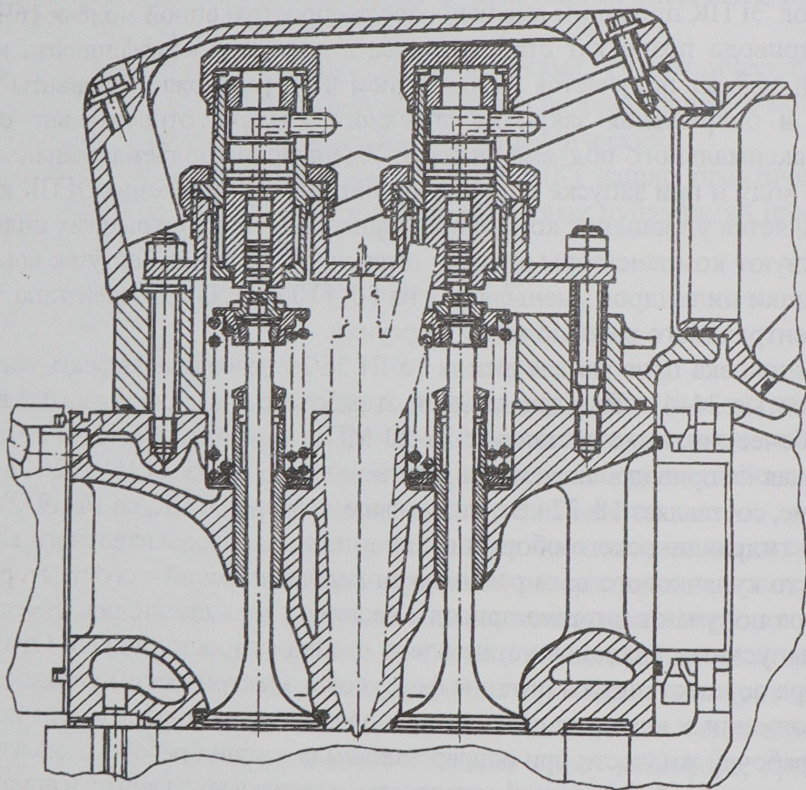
Схема установки СГЦ на цилиндровой крышке дизеля ЧН26/26 (Д49)
